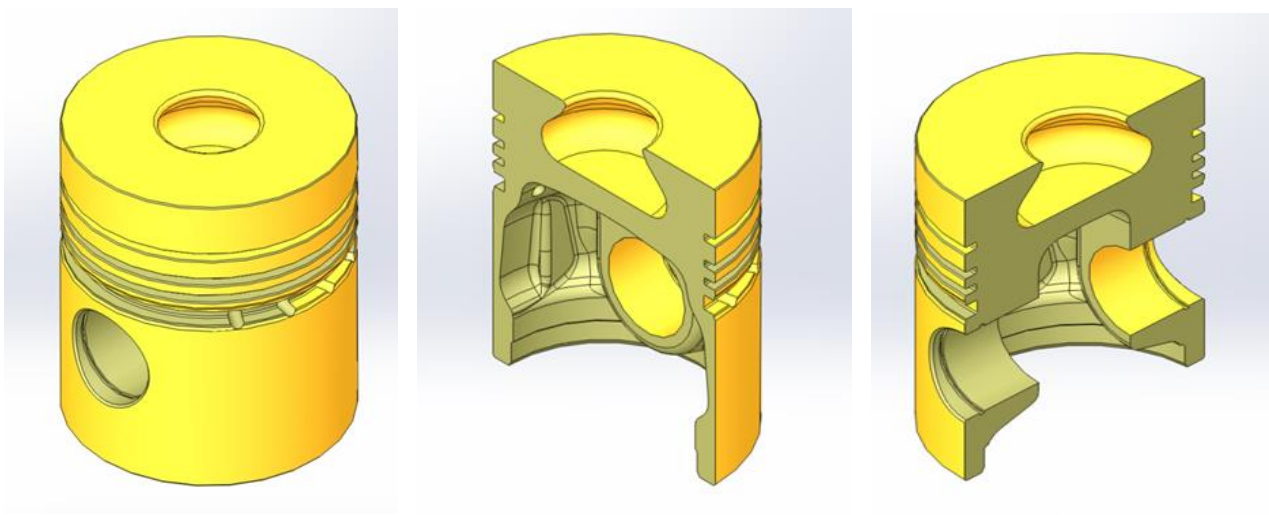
3D-модель литий деталі поршня Д 240-1004021
